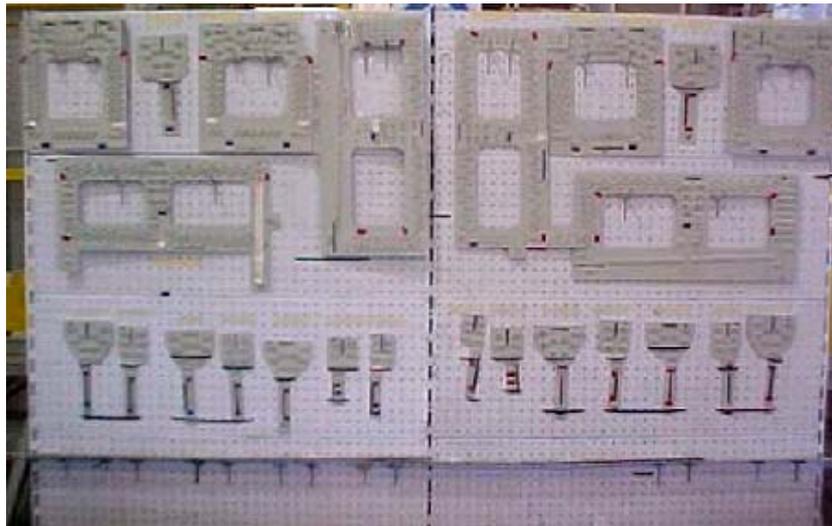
42 Soporte para plantillas en H/Stab Elevadores
